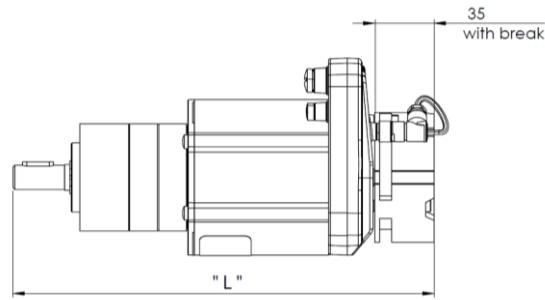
Dimensions hors tout - SWD® Core - avec frein externe
